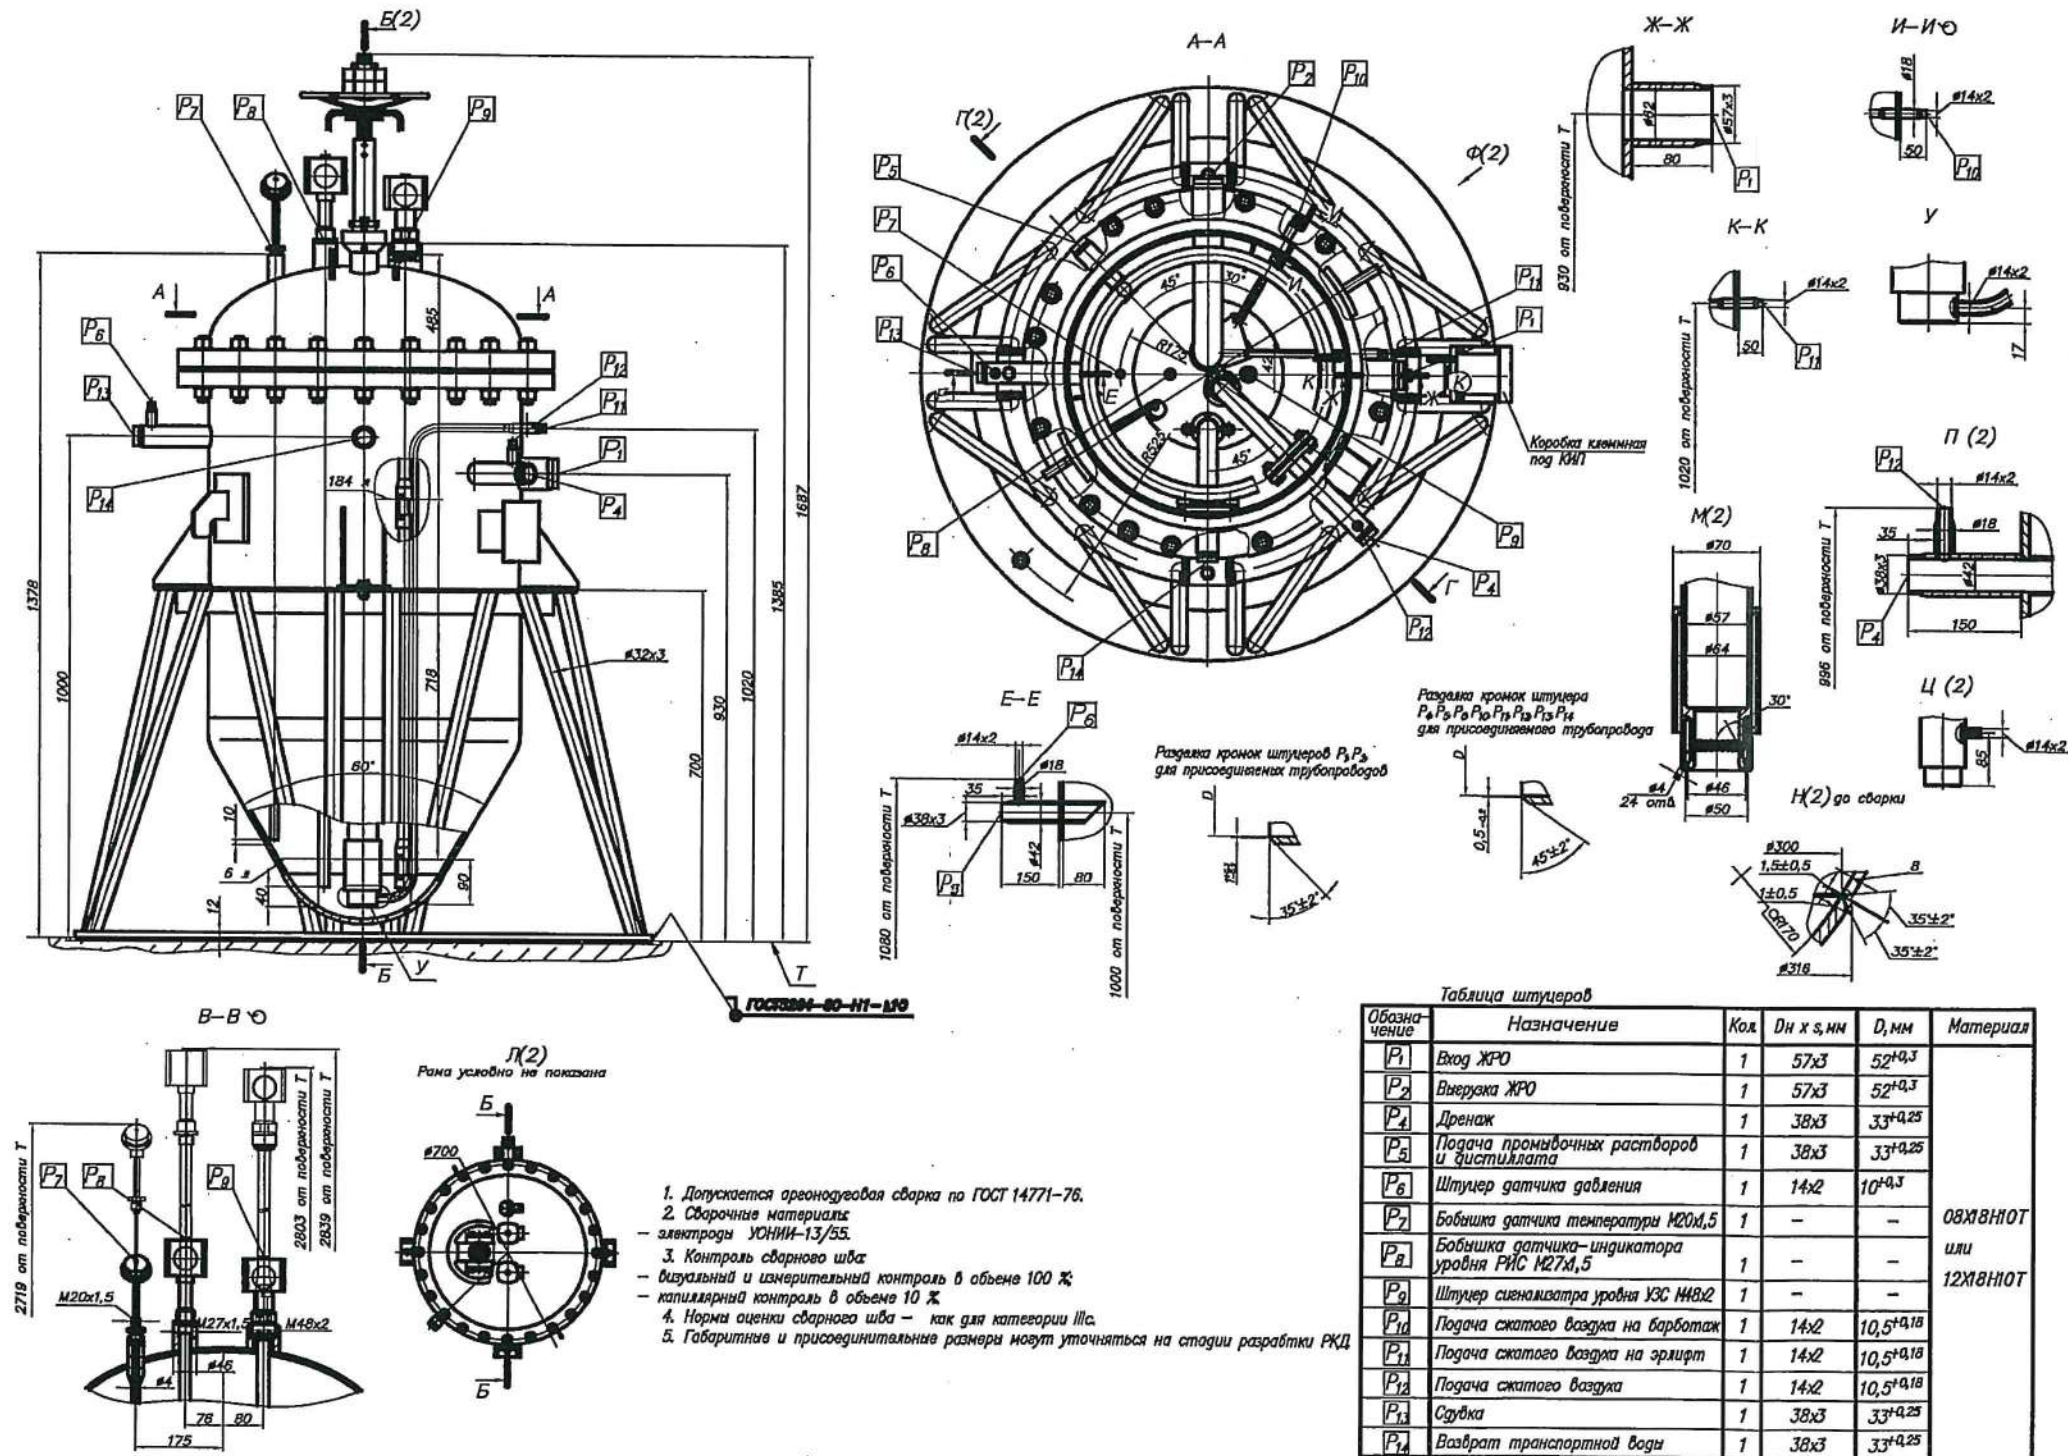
Габаритные, присоединительные размеры и конструктивное устройство мерника
